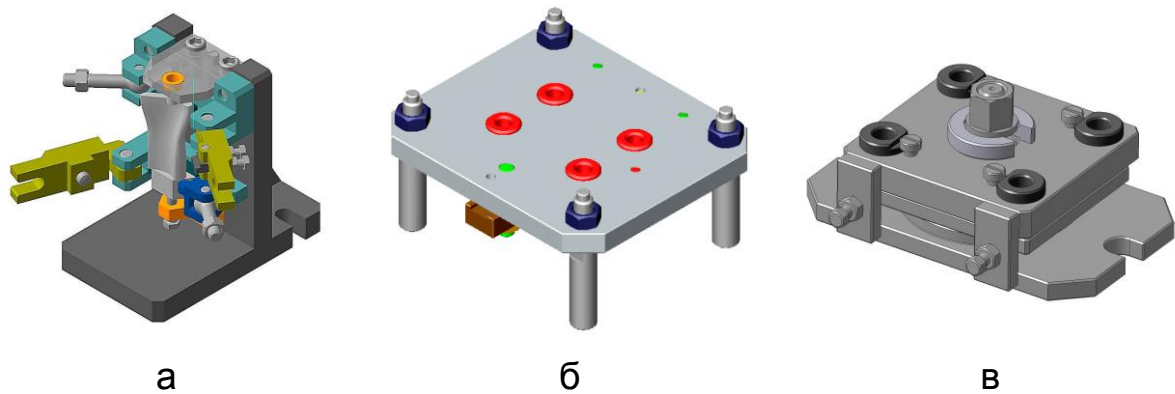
Приклади загального вигляду кондукторів різного компонування: а – корпусний; б – стійковий; в – коробчастий
